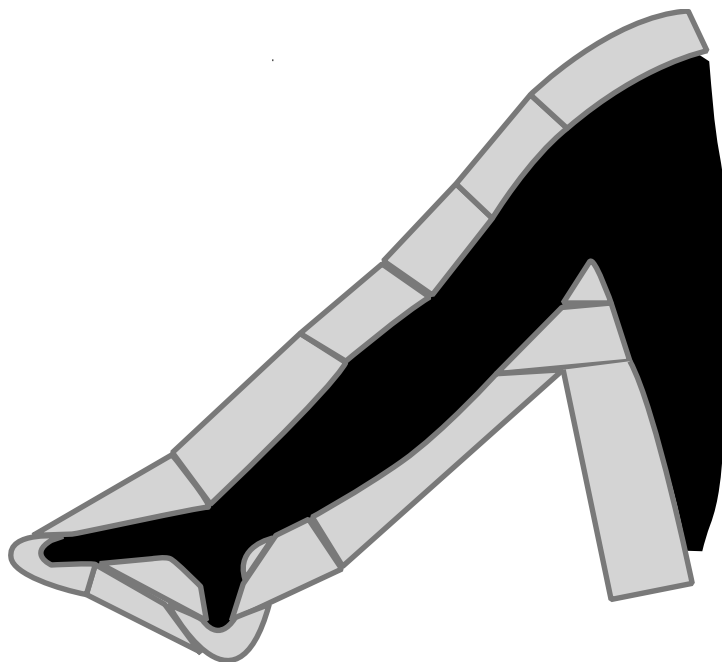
exemple schématique de moulage d'un bras à l'aide d'un moule à pièces, le moule à bon creux
